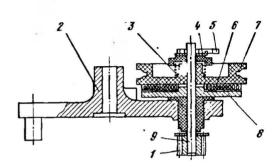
Устройство механизма реверса: 1 — зубчатое колесо механизма реверса; 2 — пружина, толкающая зубчатое колесо реверса
